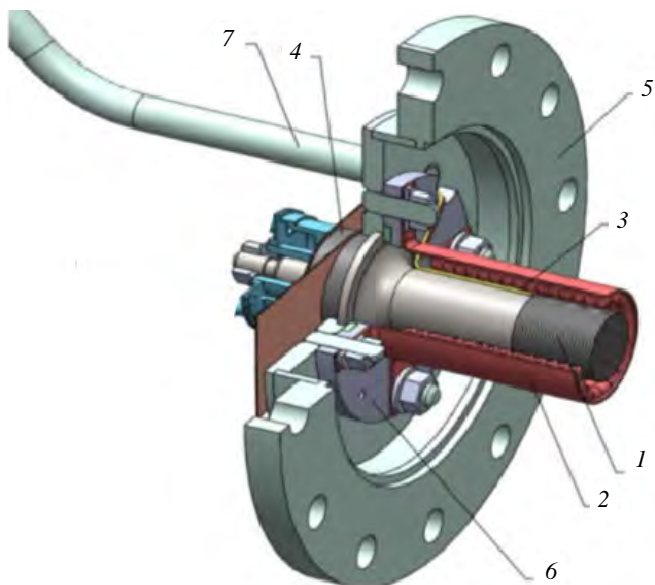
Схема ультразвукового литиевого инжектора токамака T-11M: 1 — колебательная система; 2 — нагреватель; 3 — термометр термопарный; 4 — пьезокерамический элемент; 5 — корпус инжектора; 6 — прижимной фланец с герметизирующей прокладкой; 7 — вакуумный ввод термопары и нагревателя
